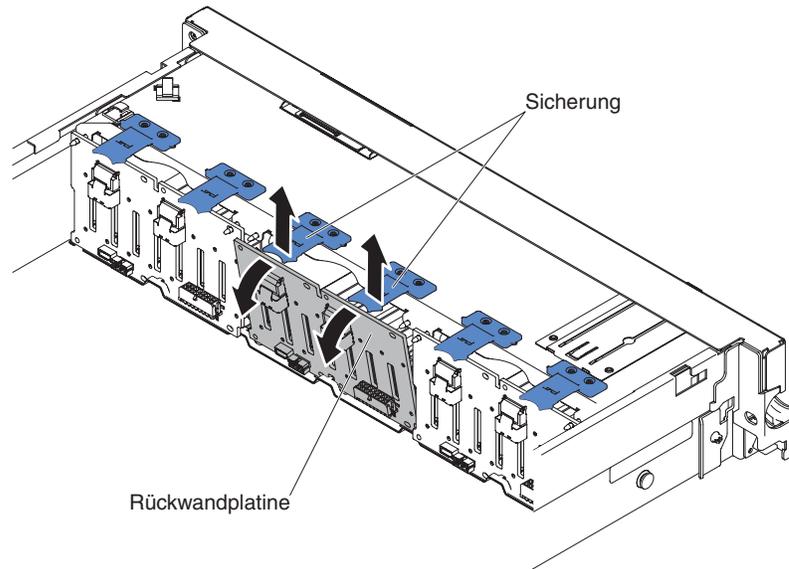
Rückwandplatine für Hot-Swap-Laufwerk entfernen
